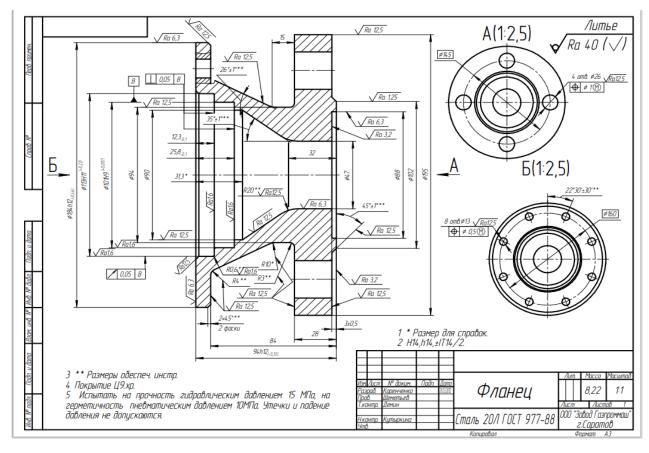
Пример конструкторского чертежа обрабатываемой детали: фланец
